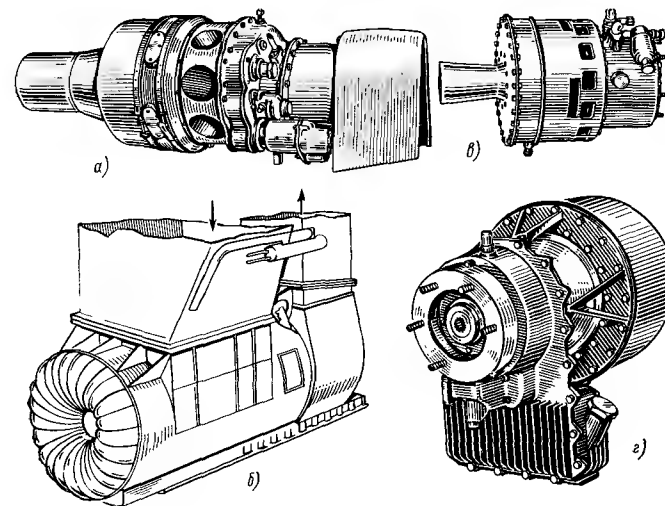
Внешний вид ГТУ с кольцевым подводом воздуха в компрессор:
